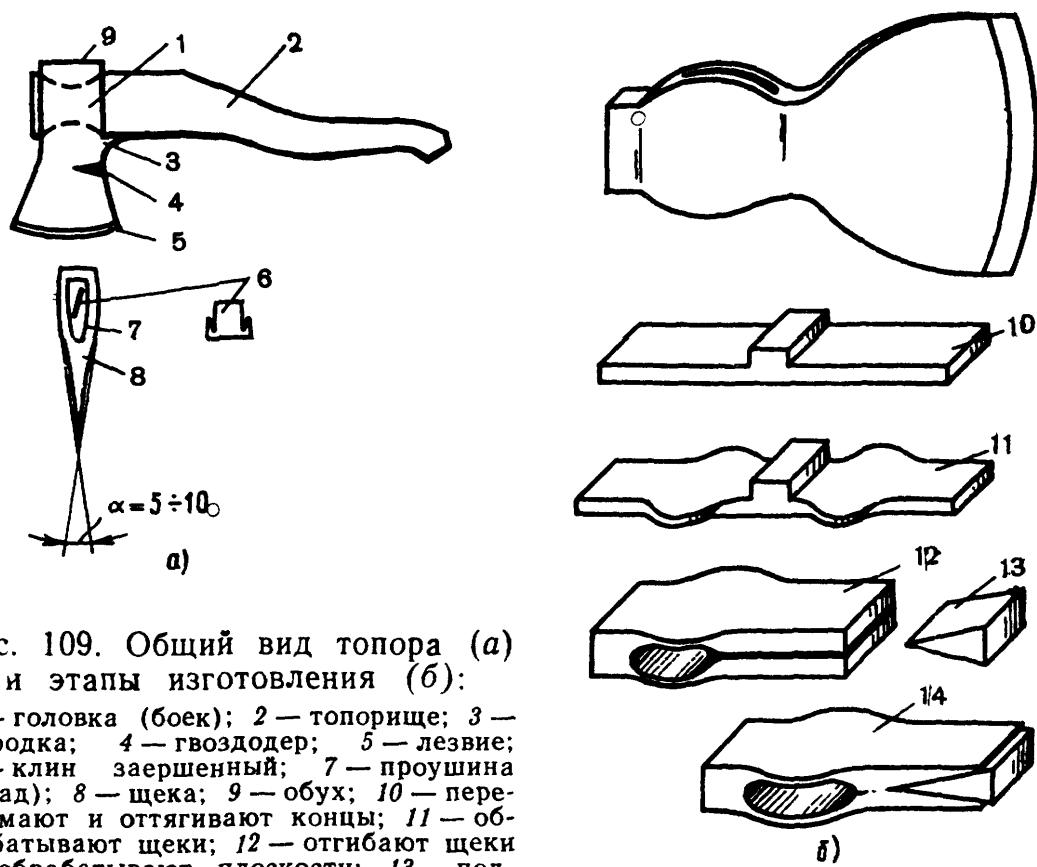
Общий вид топора (а) и этапы изготовления (б):
